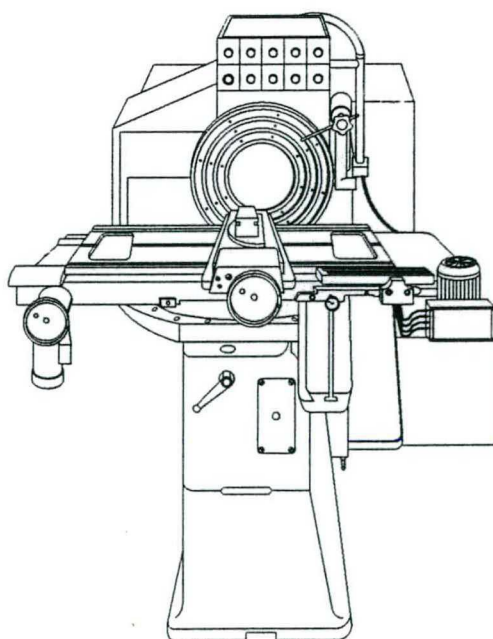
Máquina-ferramenta para usinagem de ultraprecisão Boley - década 60/70 [10].
